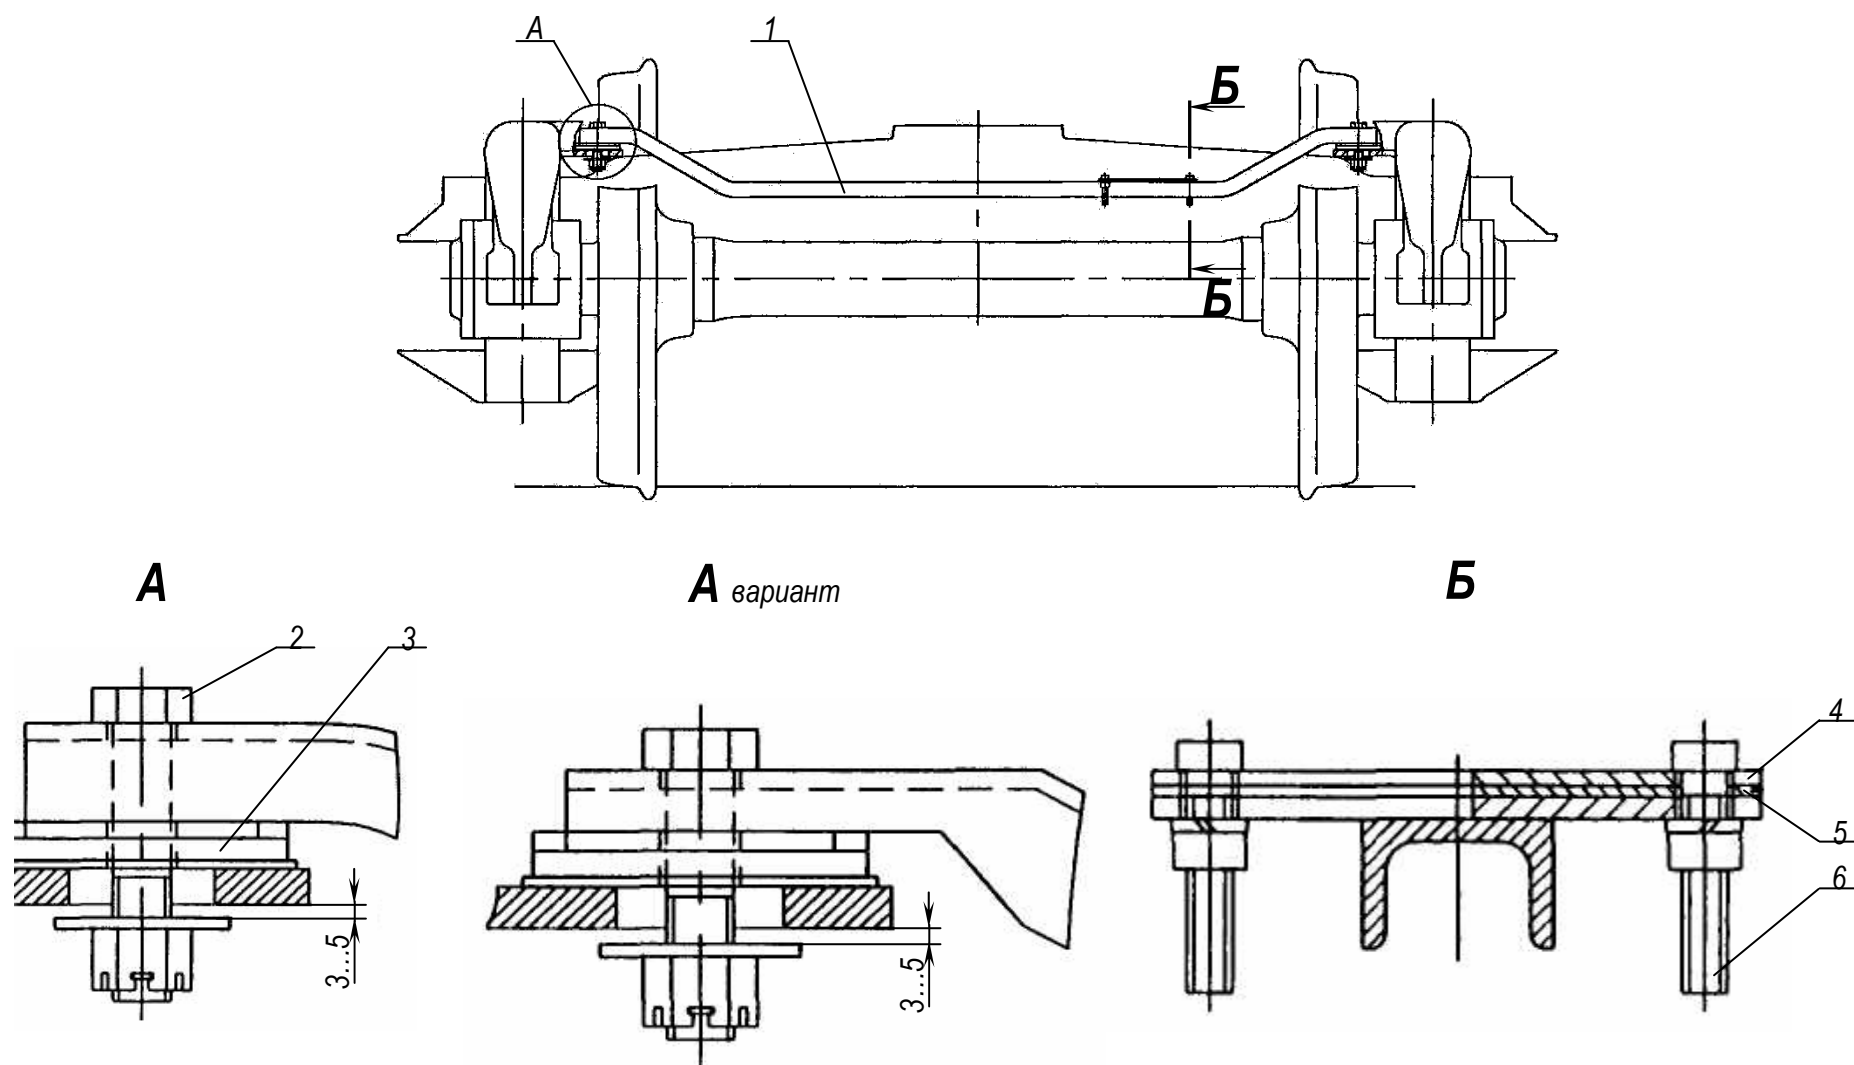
Балка опорная для авторежима: 1 – балка, 2 – болт, 3 – резино-металлический элемент, 4 – планка контактная, 5 – планка регулировочная, 6 – болт
